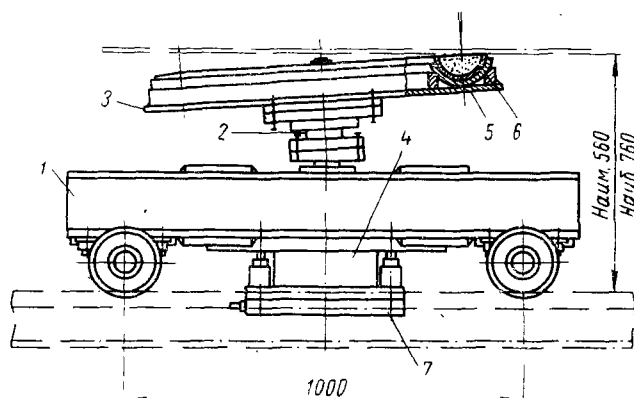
Флюсовая подушка с эластичным лотком для сварки кольцевых швов
